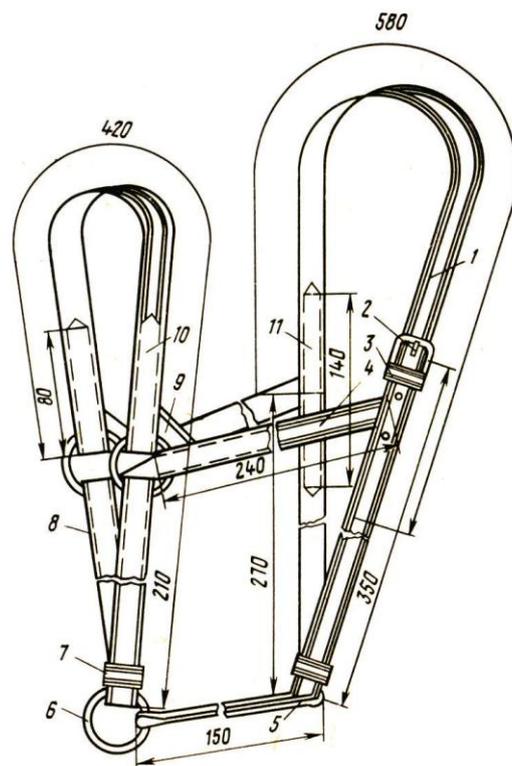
Недоуздок стоялый: 1 – ремень суголовный с подбородным; 2 – пряжка; 3 – шлевка неподвижная; 4 – ремень щечный; 5 – петля соединительная; 6 – кольцо; 7 – шлевка подвижная; 8 – ремень подгубный; 9 – ремень угловой; 10 – ремень намордный; 11 – ремень-накладка
